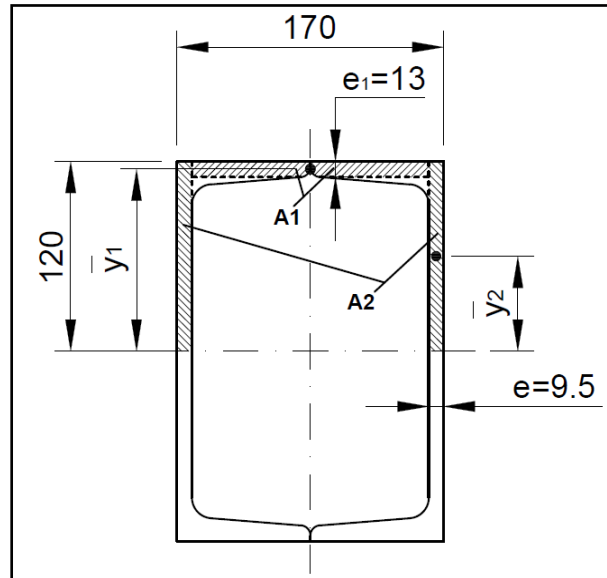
Dimensiones de la sección de las vigas longitudinales.
